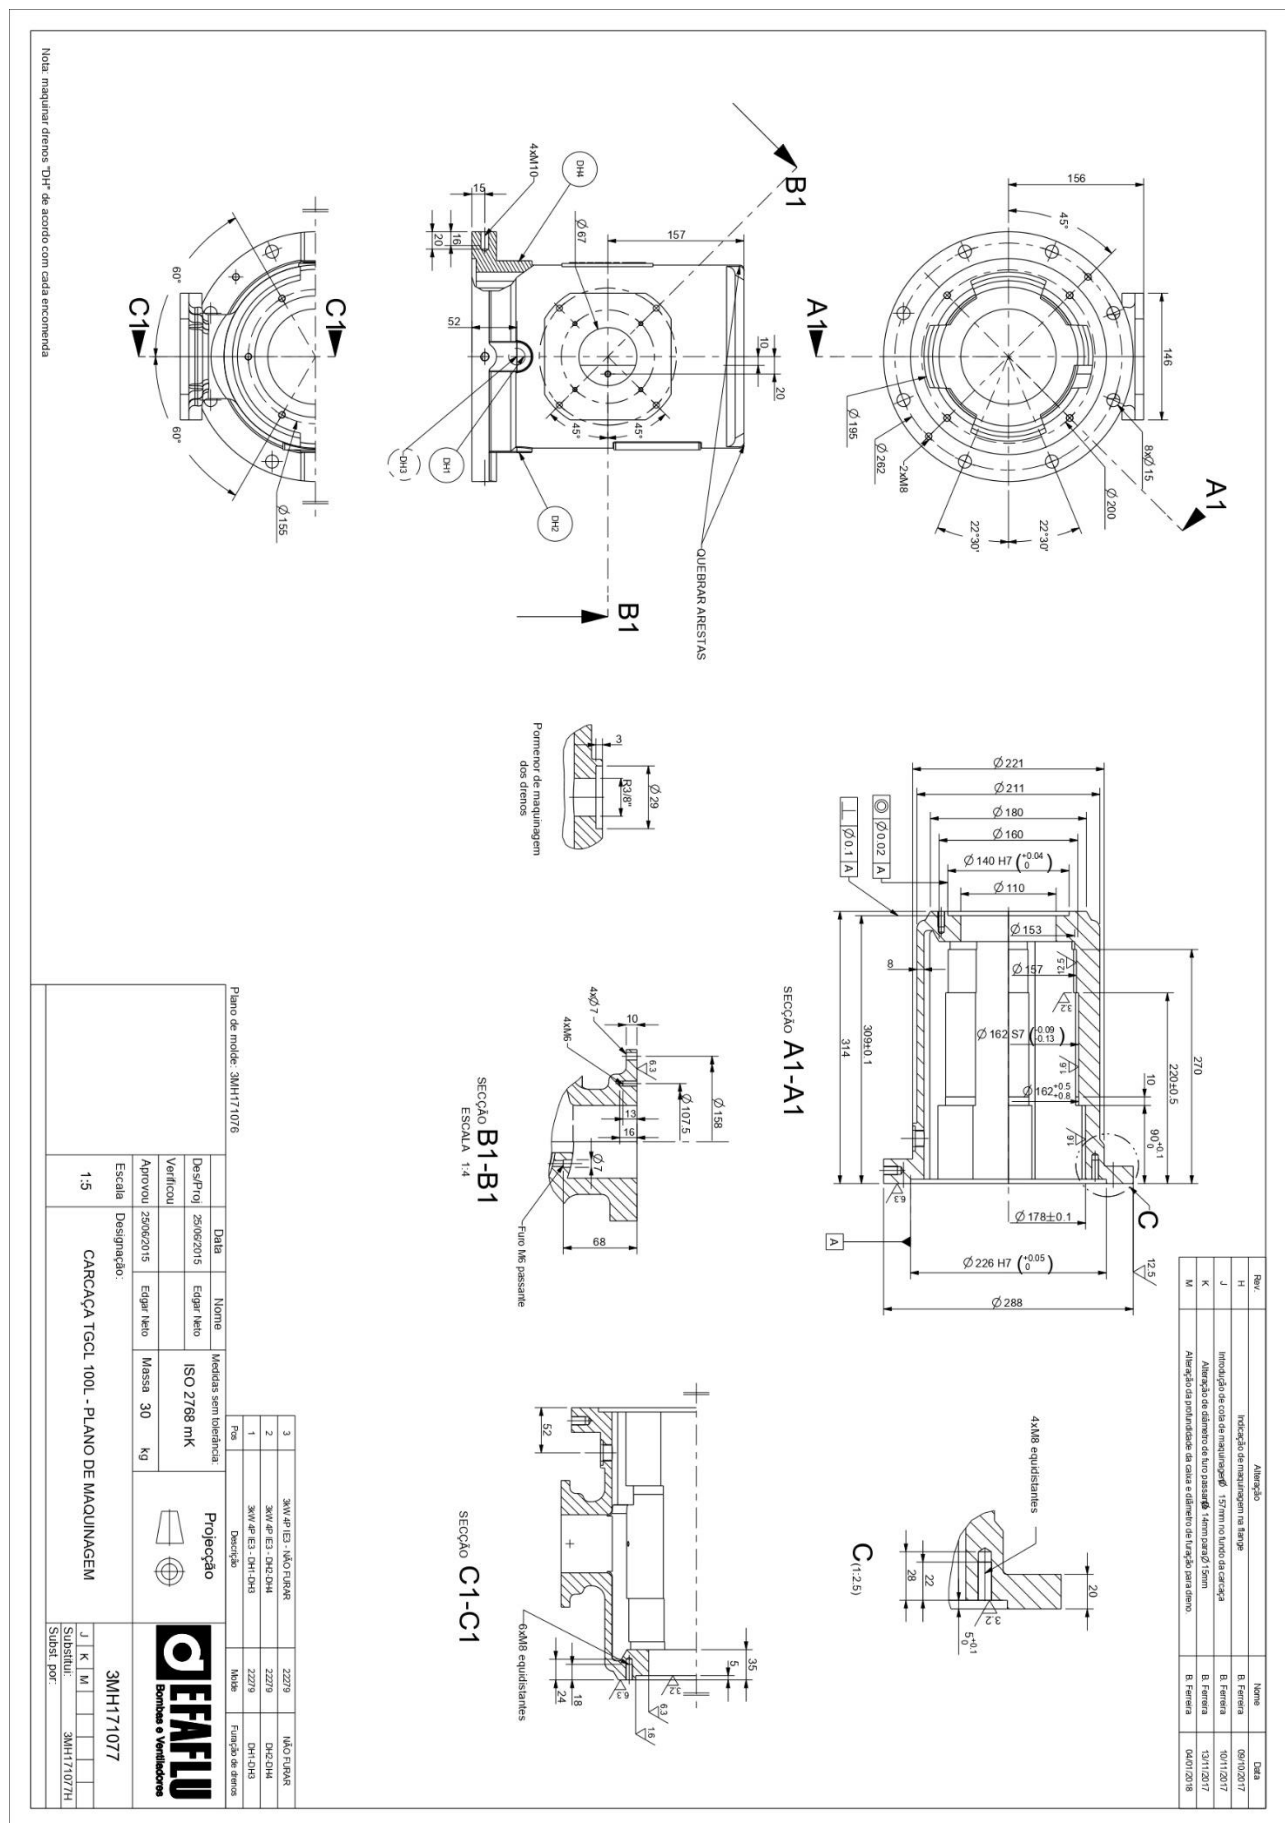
Desenho técnico da carcaça da bomba TGCL100L.
